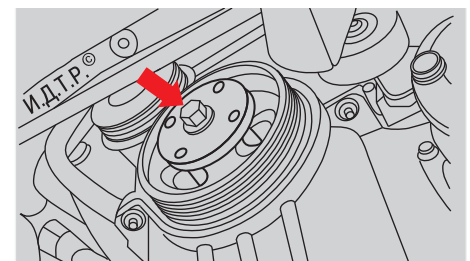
Установка шкива коленчатого вала двигателя Duratec объемом 1,3 л
